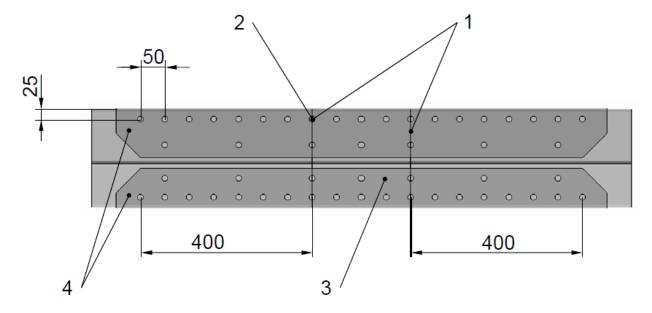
Exemple d'allongement du cadre de châssis, vue de côté
